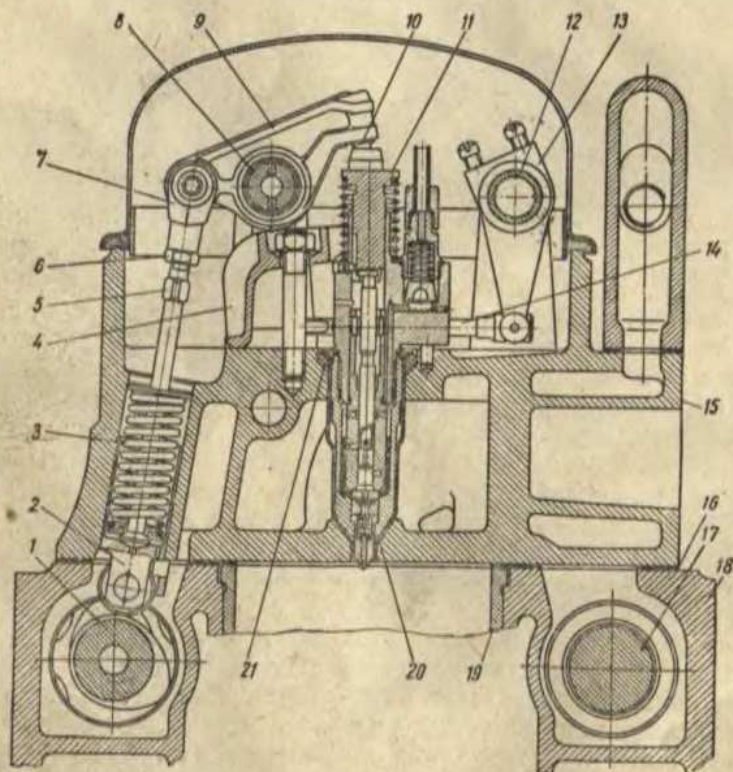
Установка насос-форсунок на двигатель и ее привод:
